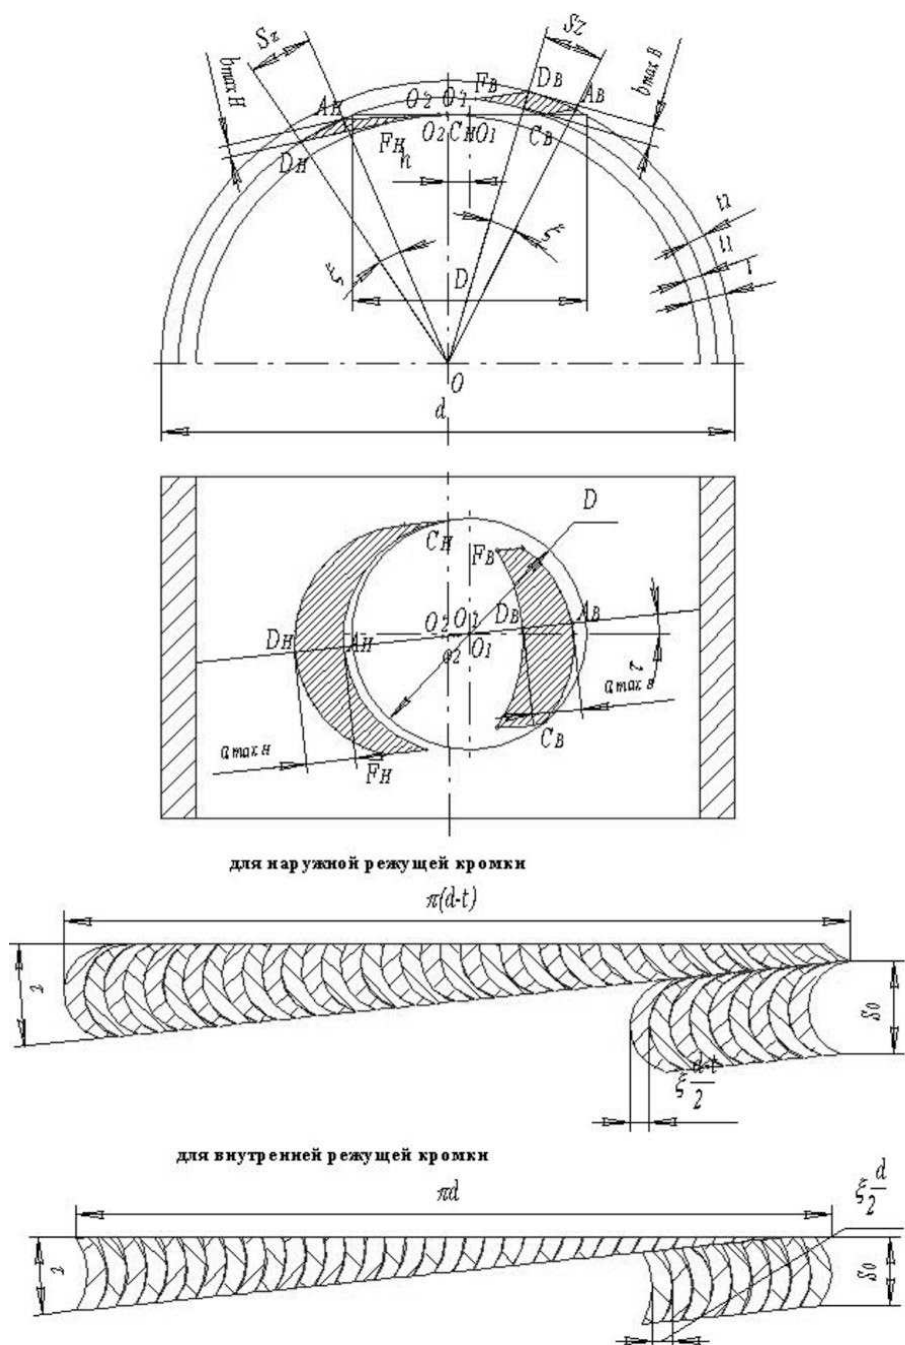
Схема образования следов при обработке внутренних поверхностей вращения торцевой фрезой с двумя режущими кромками
